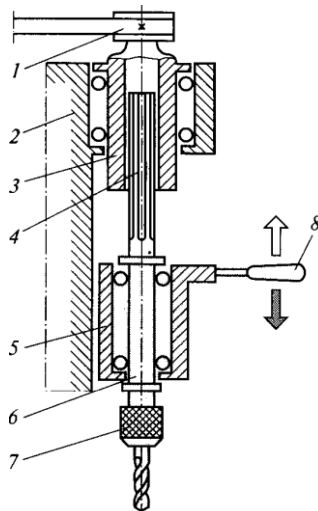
Схема складеного вертикального шпинделя: 1 – шків; 2 – станина; 3 – втулка; 4 – шліцьове з'єднання; 5 – гільза; 6 – вал; 7 – патрон; 8 – рукоятка
